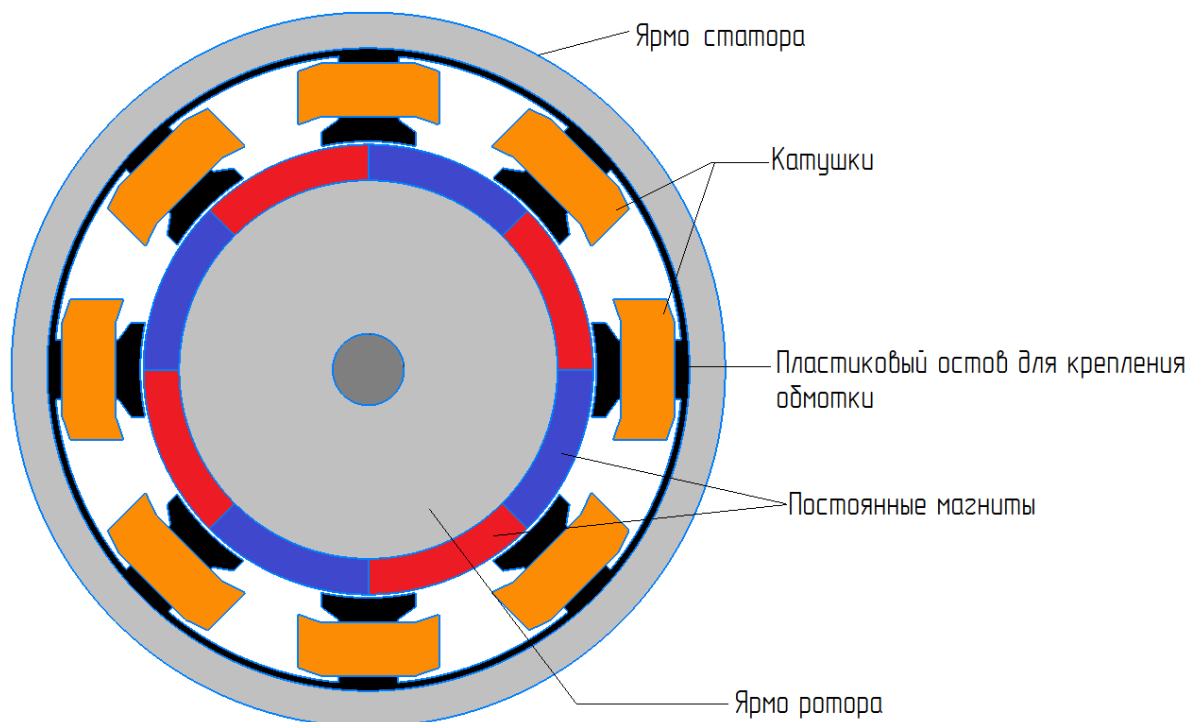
Вариант конструкции БЭМПМ с креплением обмотки на остова из немагнитного материала
